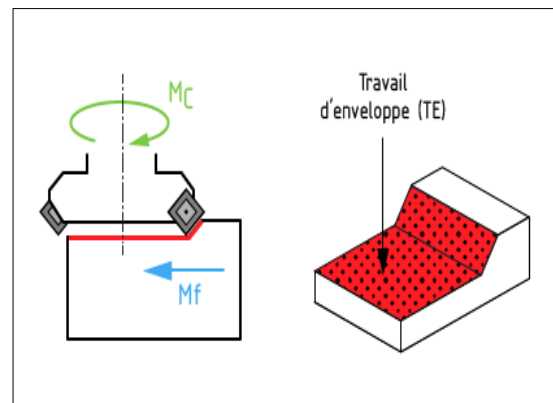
Travail d'enveloppe : fraisage d'une surface plane
